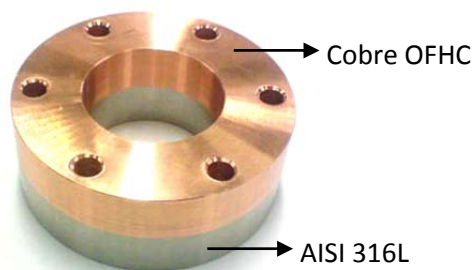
Componente bimetálico soldado por difusão e usinado para teste de estanqueidade.
